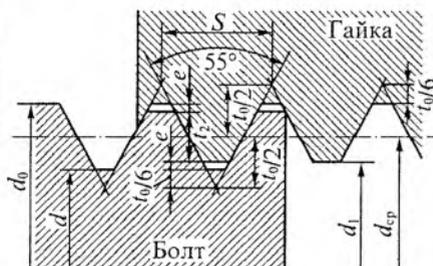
Дюймовая резьба (размеры указаны в миллиметрах): d_0 – наружный диаметр резьбы; d – внутренний диаметр резьбы болта; d_1 – внутренний диаметр резьбы гайки; $d_{\text{сп}}$ – средний диаметр резьбы; S – шаг резьбы; t_0 – высота профиля; e – нормированный зазор
